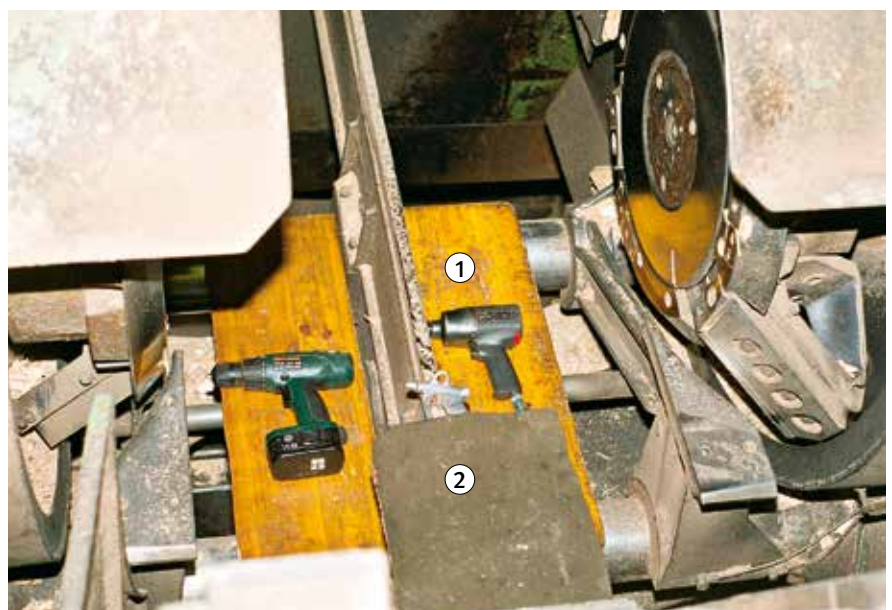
Fehlende Standfläche zum Werkzeugwechsel an einem Spaner
